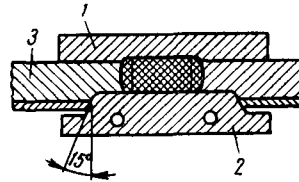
Схема электрошлаковой сварки двухслойной стали:
